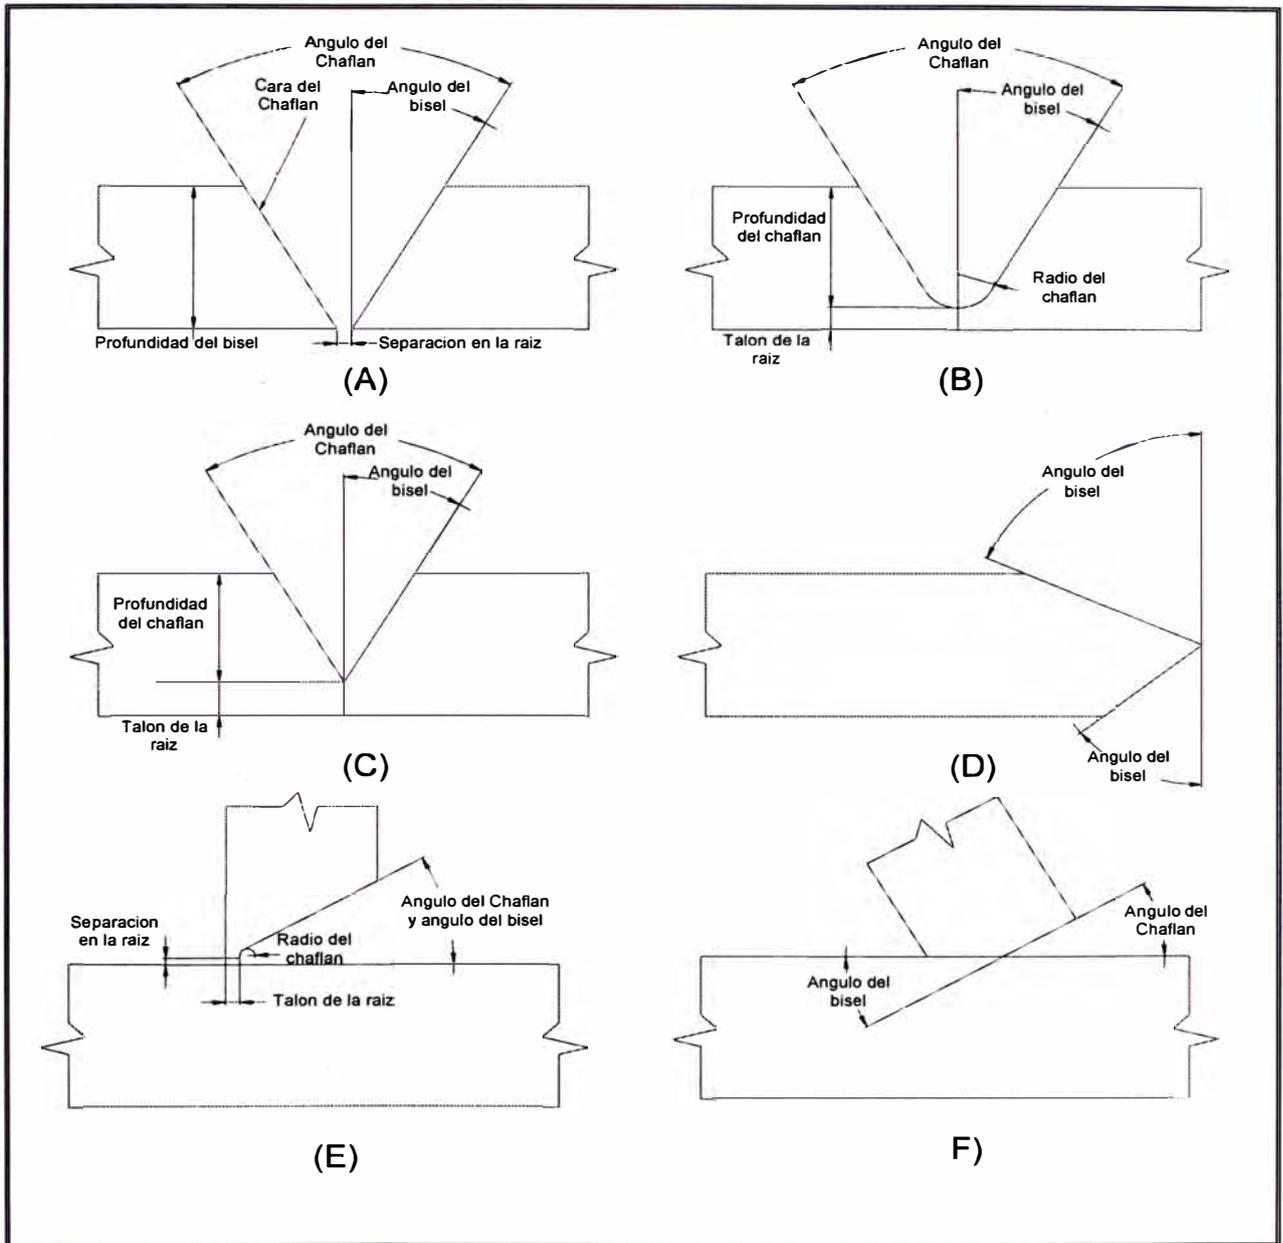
Diferentes Tipos de Soldadura
